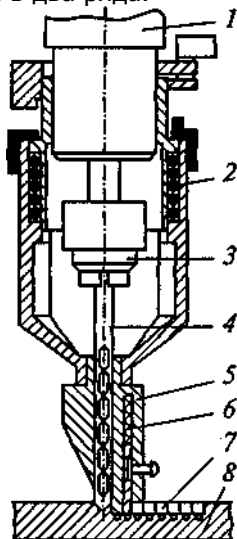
Кондуктор для сверления отверстий под фигурные вставки: 1 — шпиндель сверлильной машины; 2 — приспособление для сверления; 3 — патрон; 4 — сверло; 5 — кондуктор; 6 — фиксаторы; 7 — просверленные отверстия; 8 — деталь
